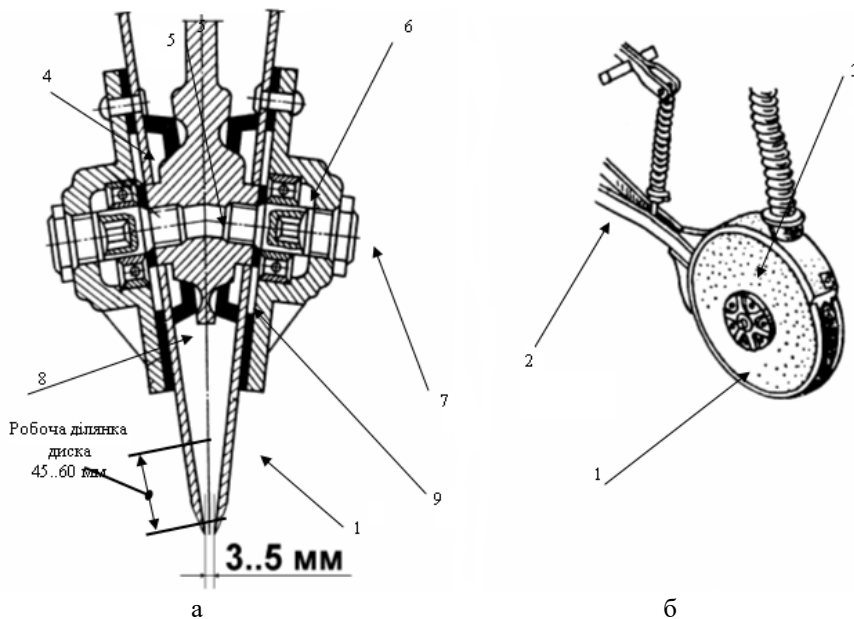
Двобічний сошник сівалки СЗ-3,6: а – схема конструкції сошника, б – зовнішній вигляд сошника, 1 – диск, 2 – корпус, 3 – система кріплення та регулювання, 4 – кришка, 5 – вісь, 6 – підшипник, 7 – заглушка, 8 – прокладка, 9 – ущільнювач
